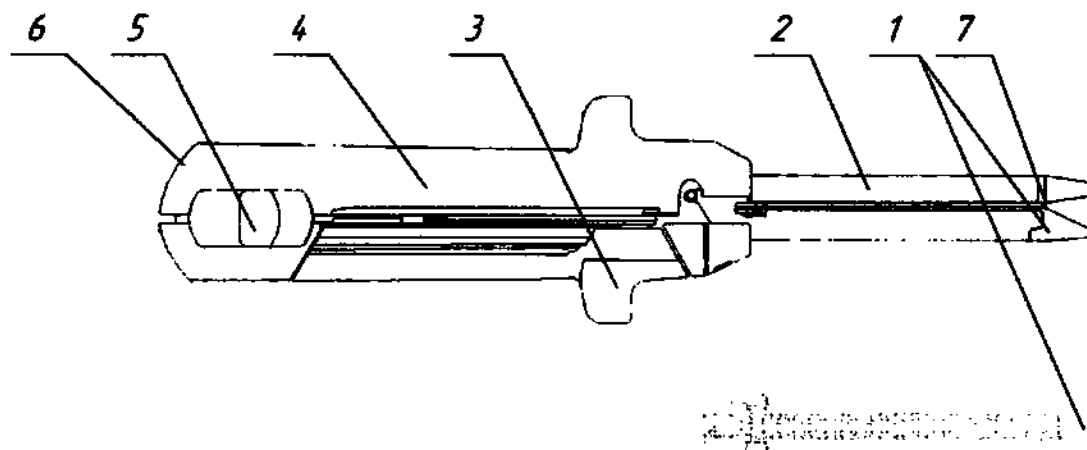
Схематичное изображение аппарата линейного сшивающе-режущего «Тип Двойная кнопка» и сменной кассеты: 1 – Сменная кассета; 2 – Матрица; 3 – Фиксирующая рукоятка; 4 – Корпус аппарата; 5 – Рычаг прошивания; 6 – Кнопка размыкания; 7 – Стопорный штифт;
